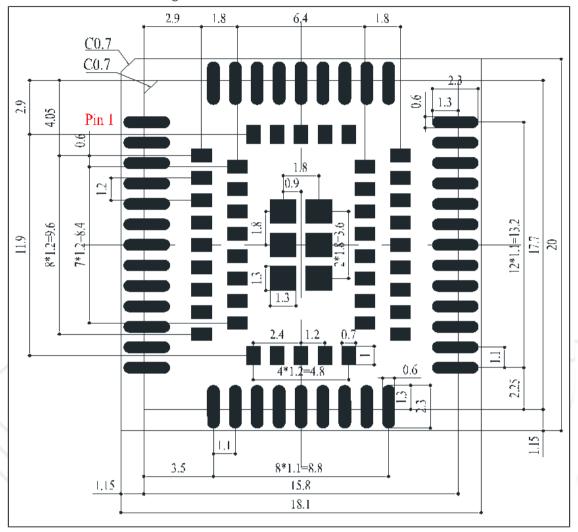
PCB焊盘兼容尺寸(单位: mm)
